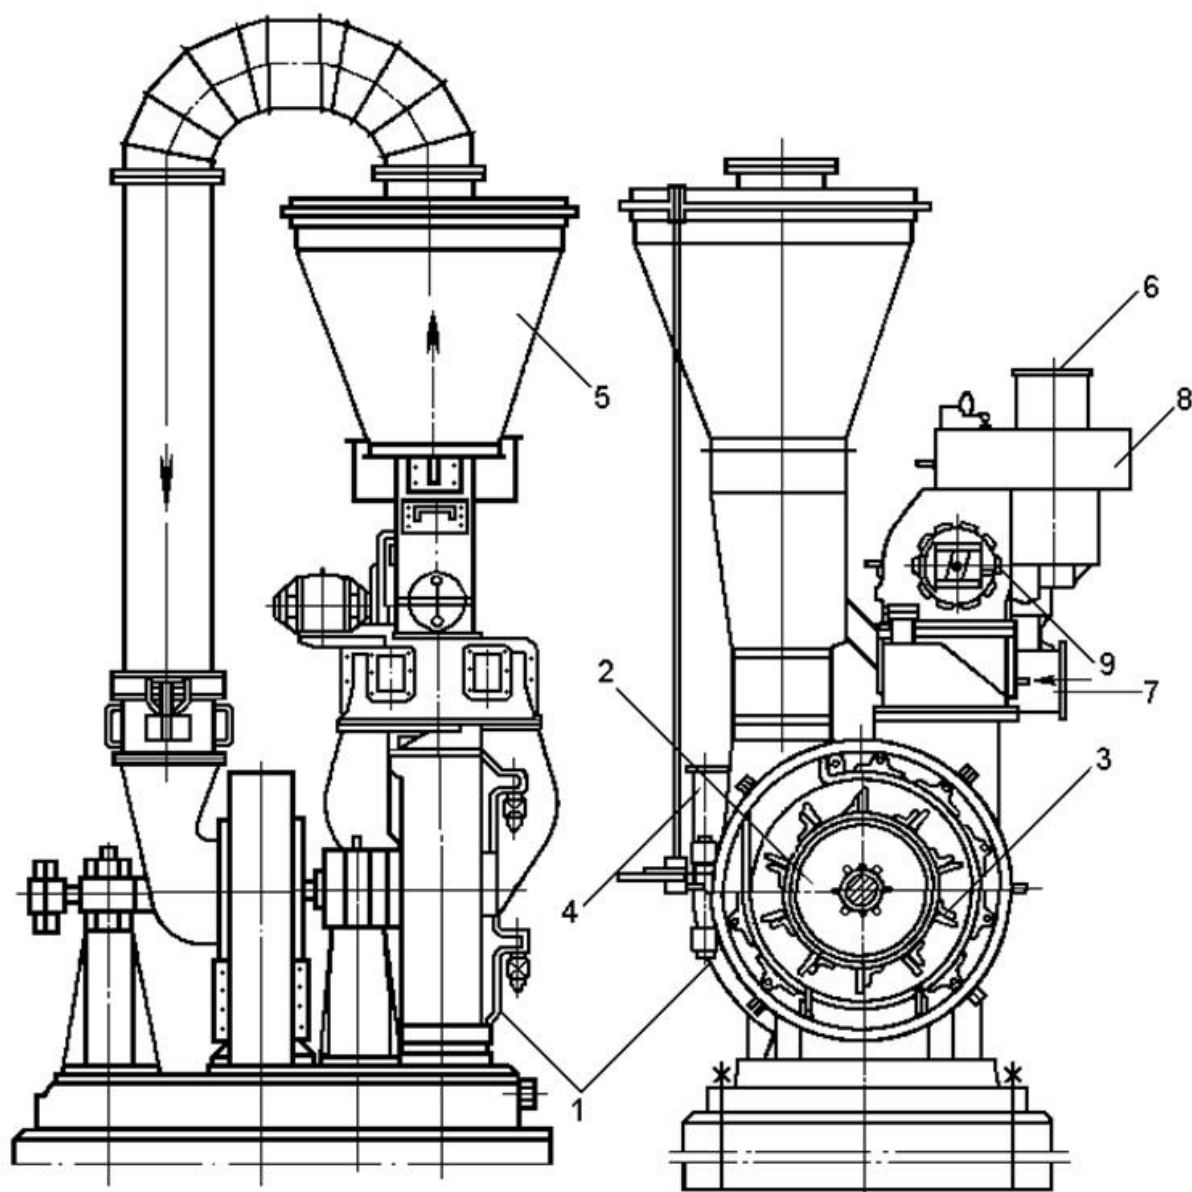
Схема размалывающей установки с крестовой мельницей:
